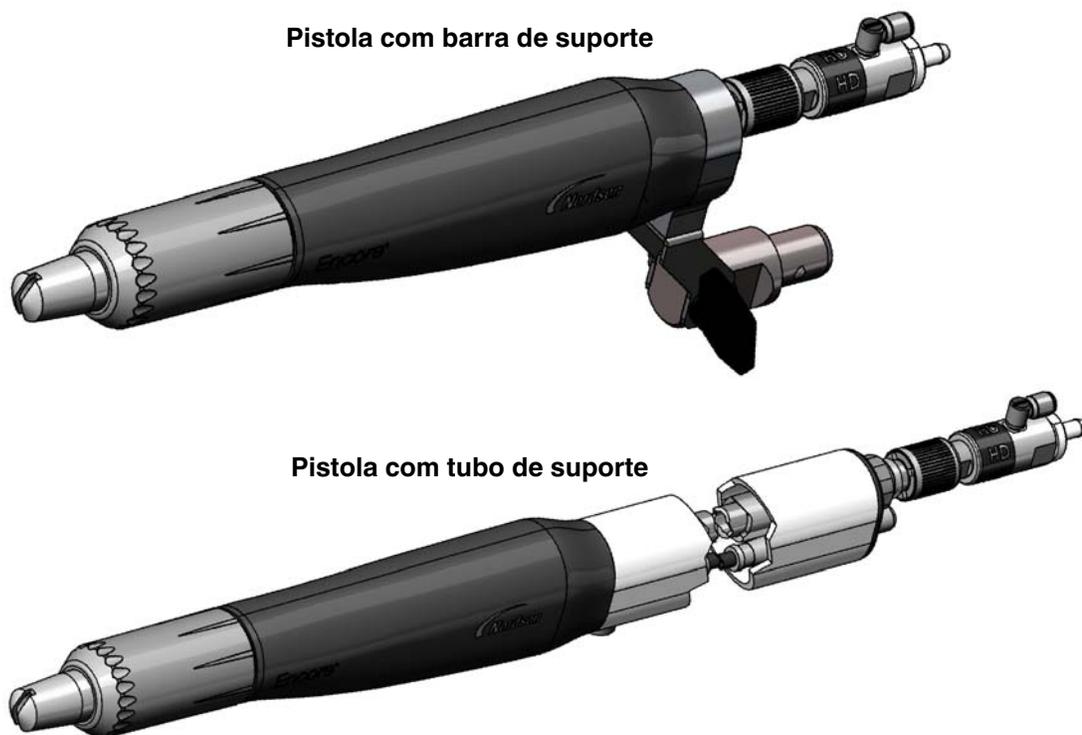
Pistolas com barra de suporte e com tubo de suporte
